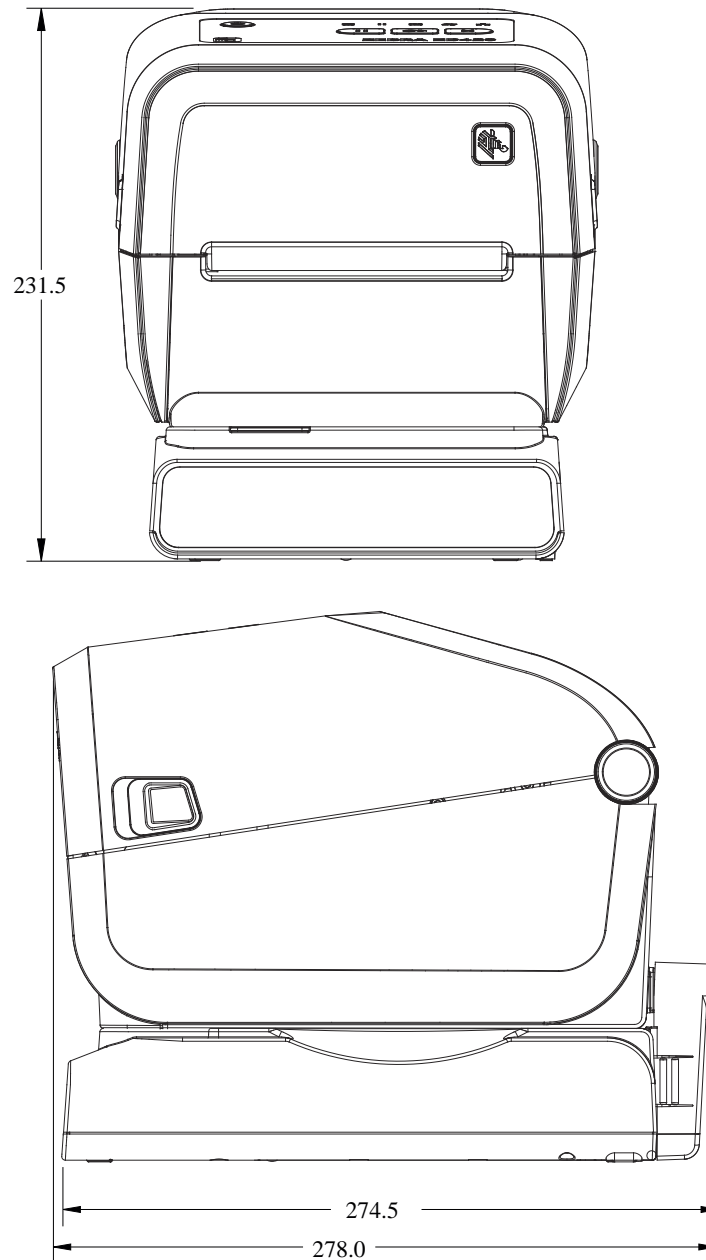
Modelos de impressora ZD421C (Transferência térmica do cartucho de fita) – dimensões da impressora com a base da fonte de alimentação conectada
